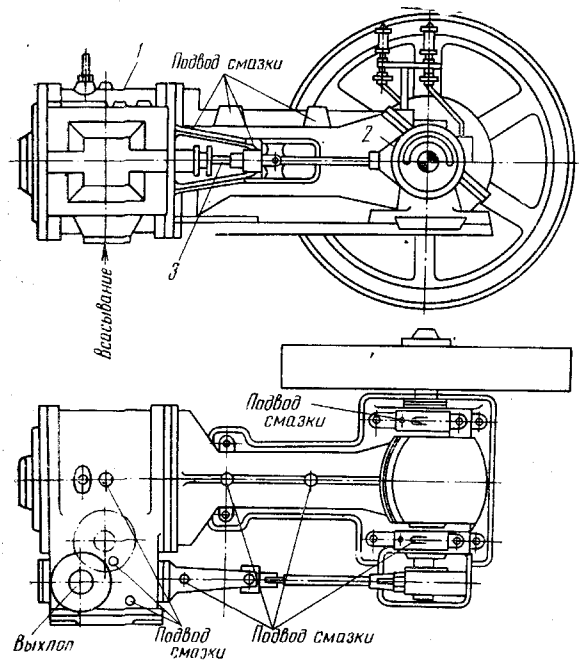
Поршневой одноступенчатый суховоздушный вакуум-насос марки ВНС-250:
